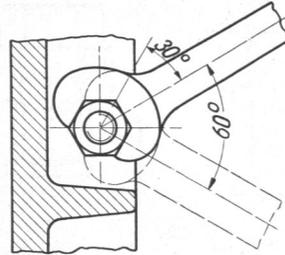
Für den Schraubenschlüssel ist genügend Platz vorzusehen.
